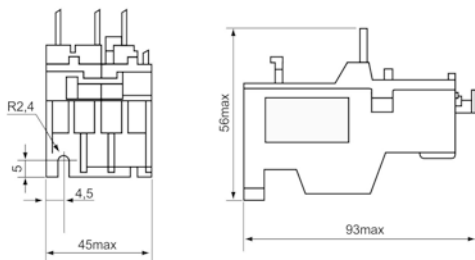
Габаритные размеры реле РТЛ 1001÷1022
